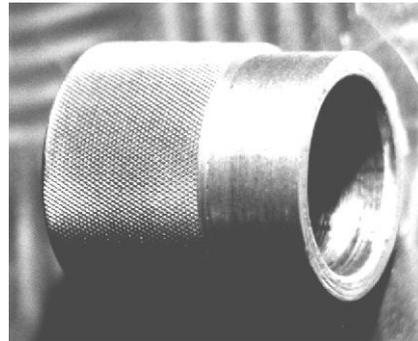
Treibwerkzeug f. Gabel-Simmerring
